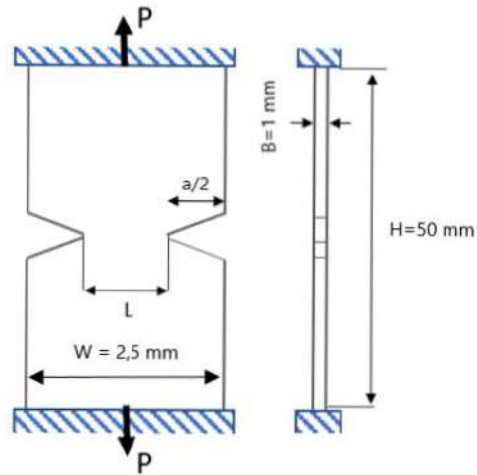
Geometría y dimensiones de las probetas utilizadas en ensayos de fractura.
